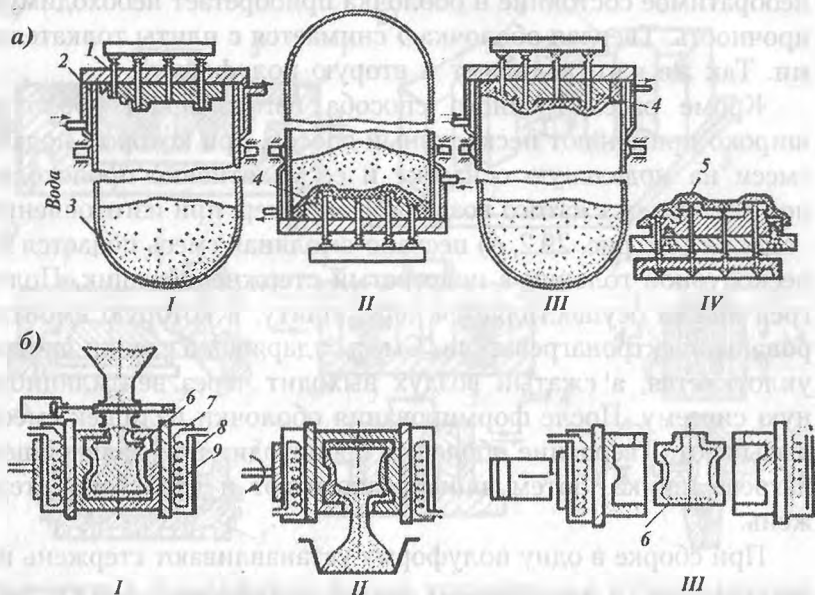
Схема процесса изготовления оболочковой формы (а) и оболочкового стержня (б)
